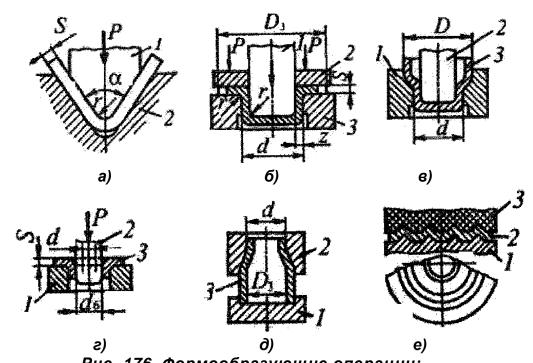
Формообразующие операции: а — гибка; б — вытяжка; в — многопереходная вытяжка; г — отбортов-ка; д — обжим; е — формовка; 1 — матрица; 2 — пуансон; 3 — заготовка
